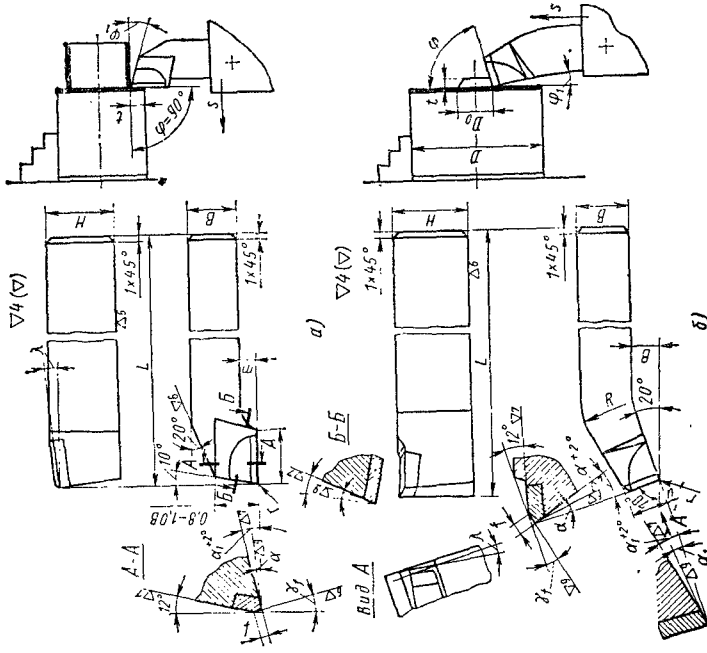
Токарные резцы, оснащенные пластинками твердого сплава:
